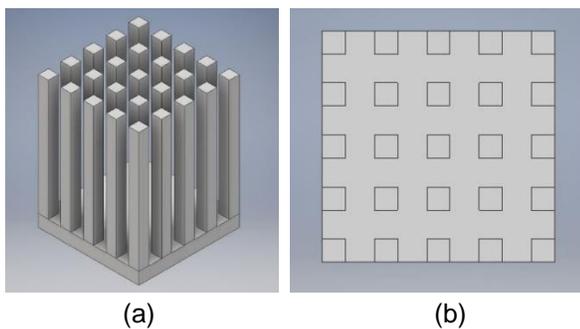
a) Vista isométrica del disipador, b) vista frontal del disipador.
